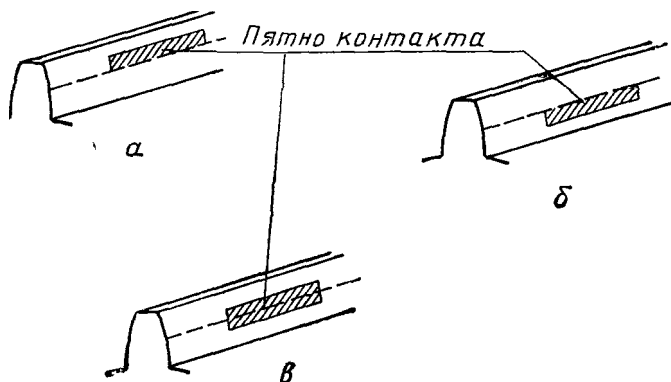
Проверка правильности зацепления зубьев в коробке перемены передач:
